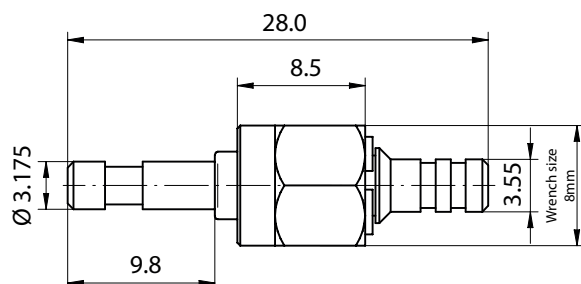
F-SMA Steckverbinder mit 6-kant Mutter
